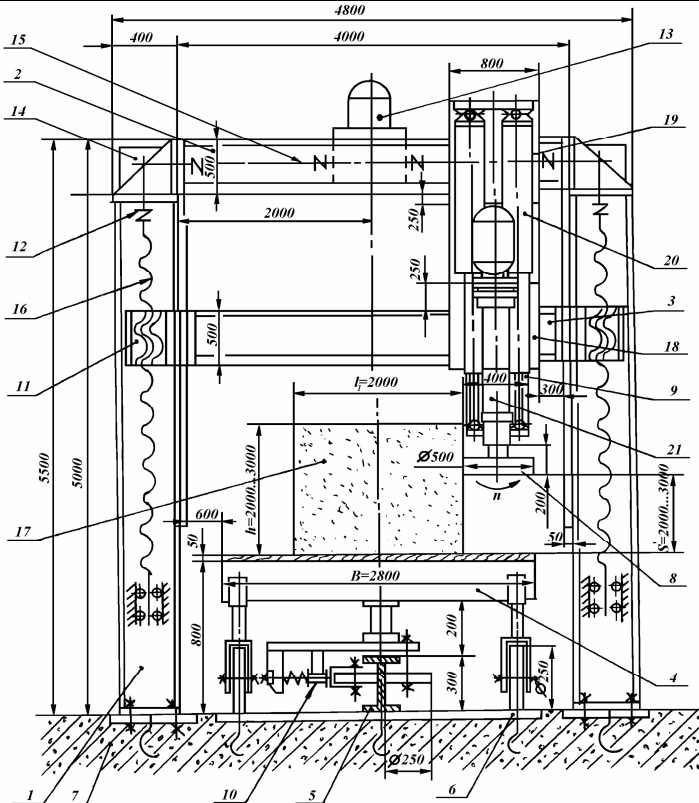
Схема конструктивно-компоновочного рішення портального верстата з криволінійним рухом робочого столу: 1 – колона;
